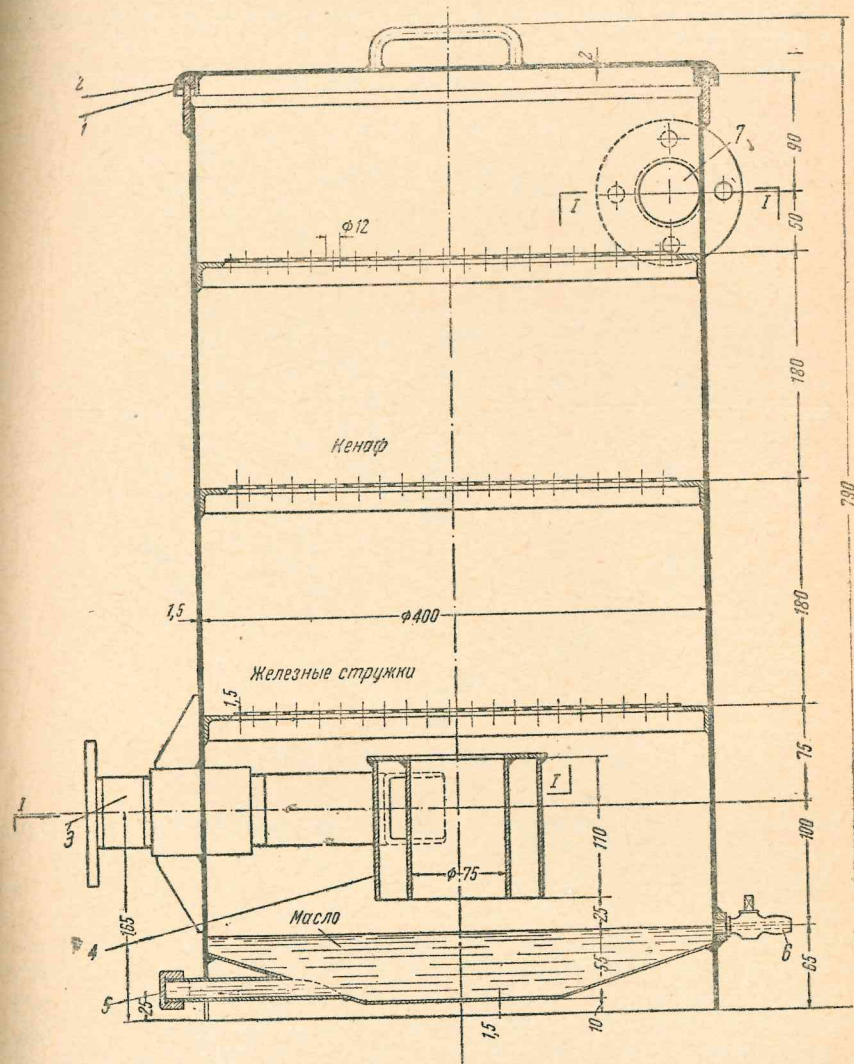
Сухой очиститель установки ЦНИИВТ-3 (продольный разрез)
